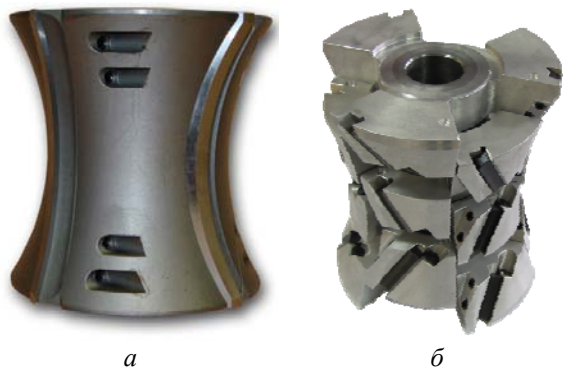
Фрезы для получения криволинейных поверхностей:
